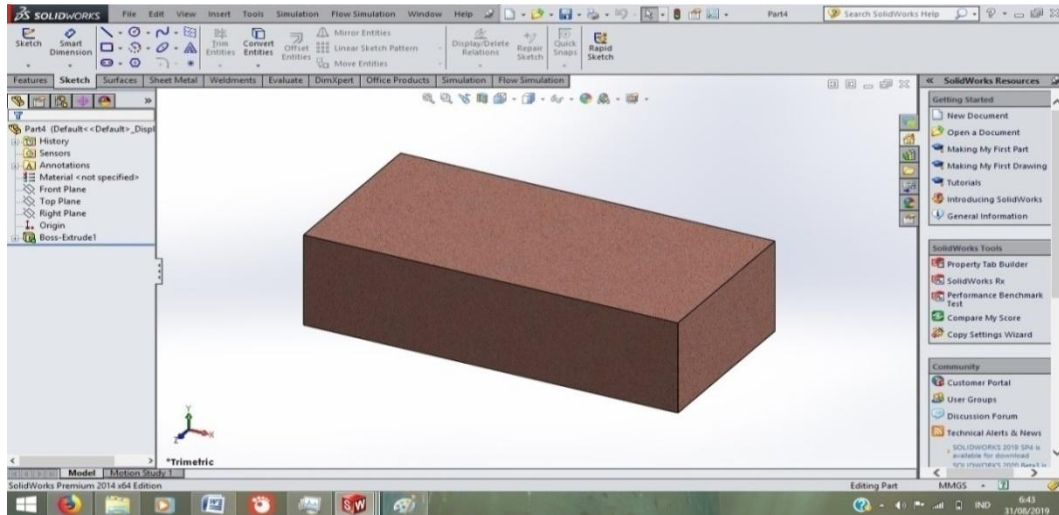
Sketch* Desain Lantai Batu SK 34
